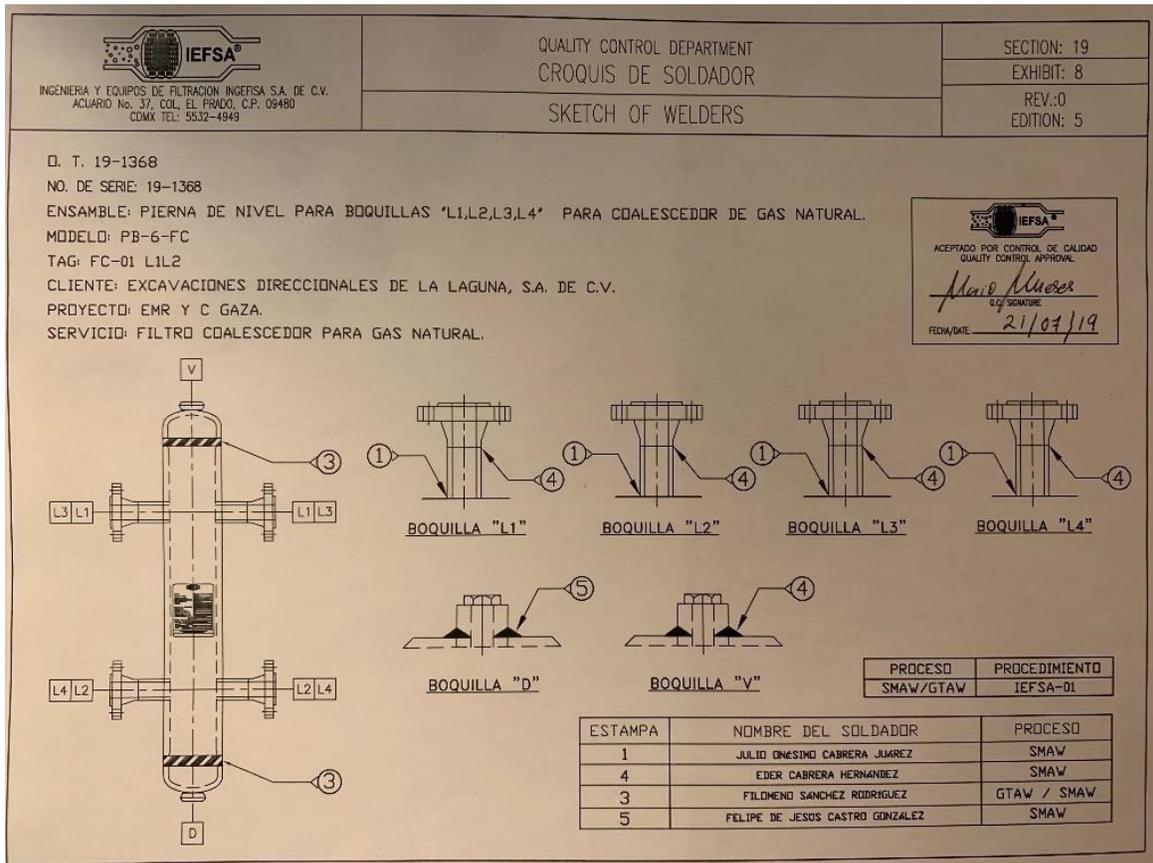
Planos de las líneas de soldadura para un recipiente de filtro coalescedor.
